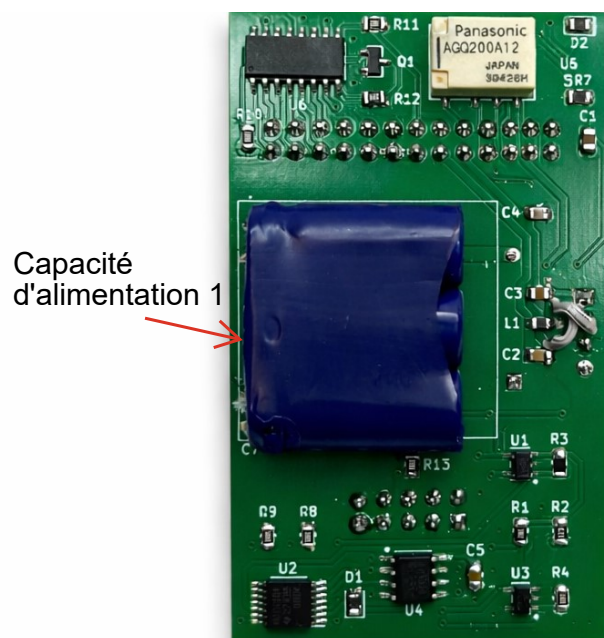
PCB de contrôle des capacités – vue face 1.
